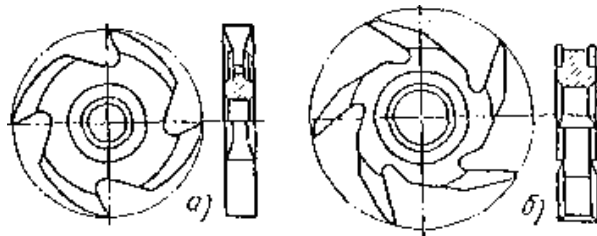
Насадні цільні фрези до чотирибічного поздовжньо-фрезерного верстата затиловані (а) і з прямою задньою гранню зубів (б)
